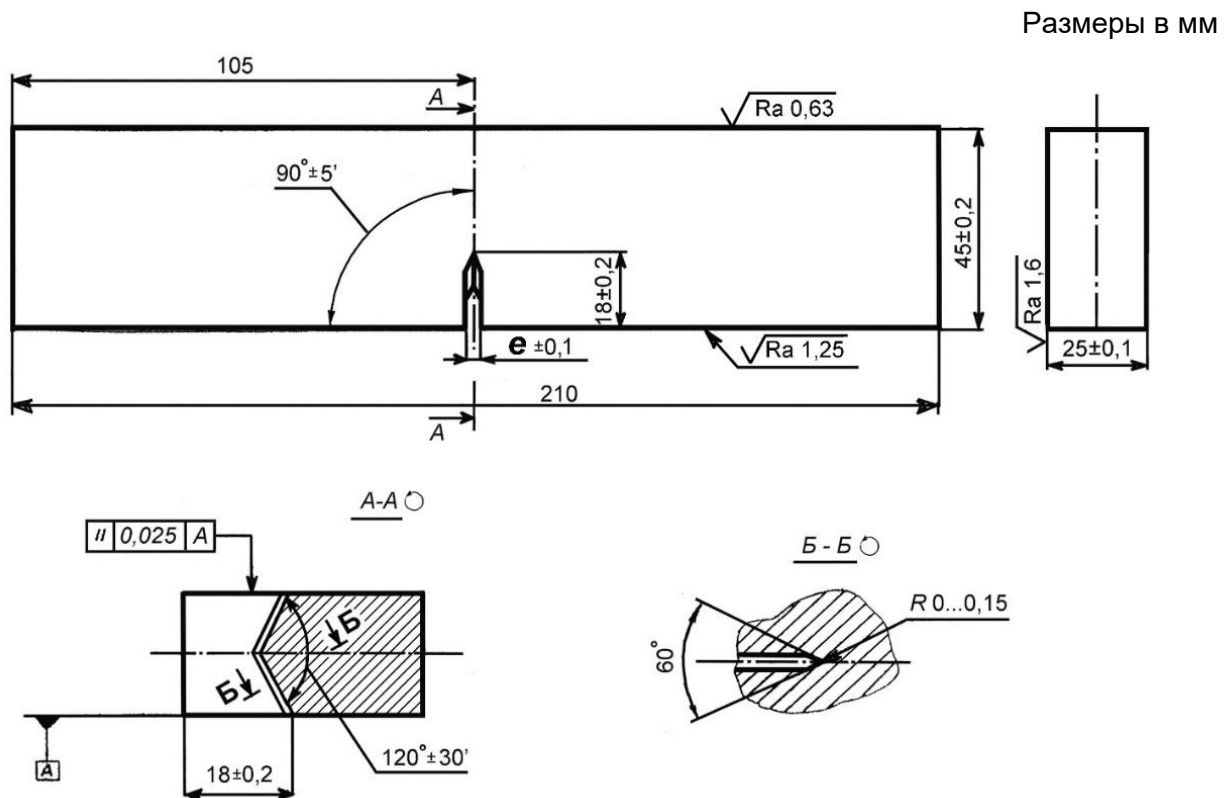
Вид и основные размеры образца для испытаний на статическую трещиностойкость
